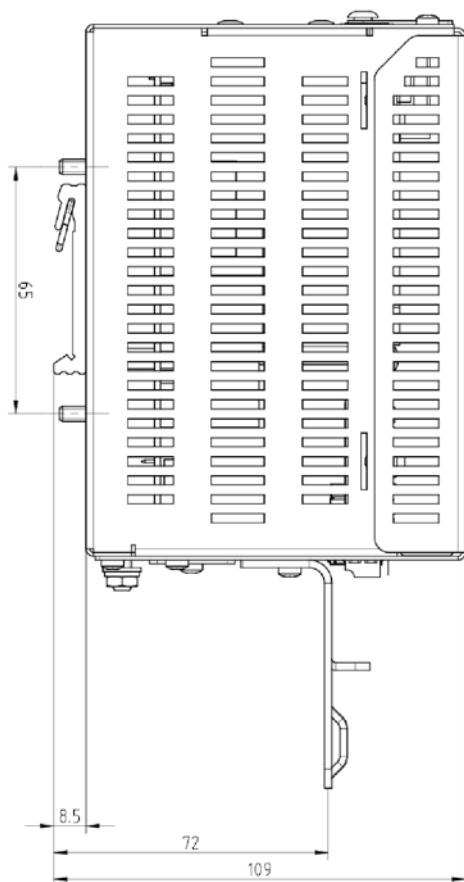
Dessin coté du switch IE X302-7EEC - Vu de côté
